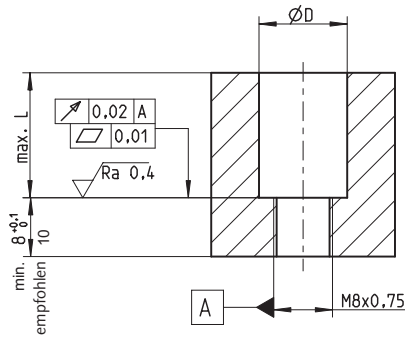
Einbau brennraumbündig. Bohrung $\varnothing$ gemäß Werkzeug Bild 5 oder Bild 6
